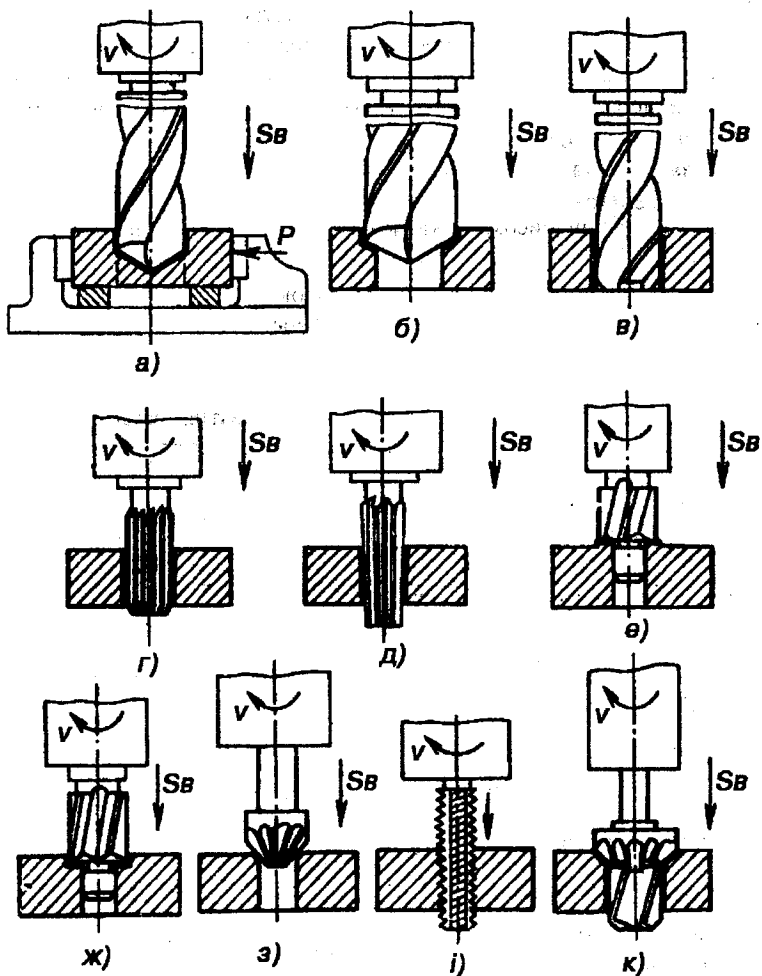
Схеми обробки заготовок на вертикально-свердильних верстатах
